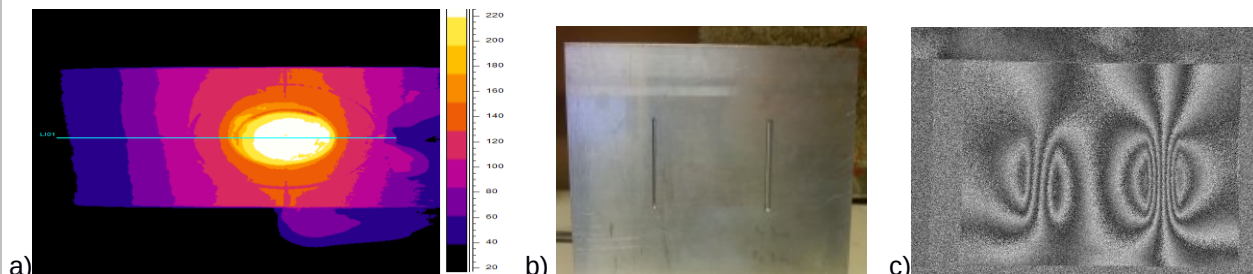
Suivi d'un rivetage par thermographie infrarouge (a), plaque de métal comportant des défauts en face arrière (b), détection de ces défauts par shearographie sur la face avant (sollicitation thermique) (c)
